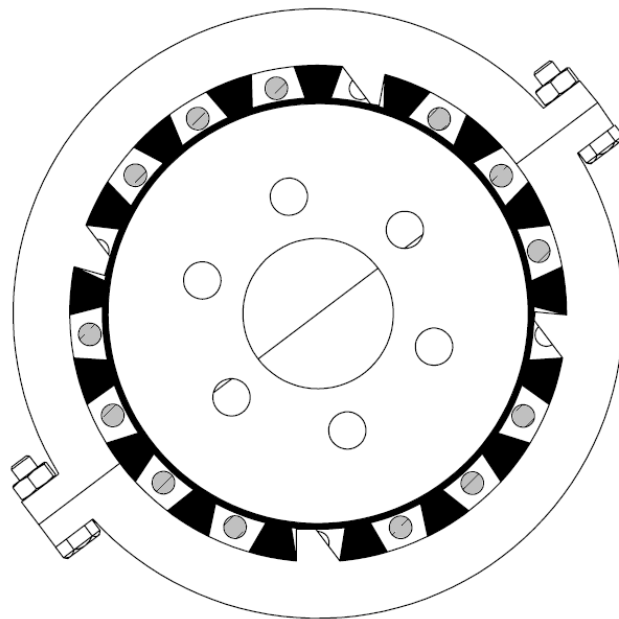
Vue du dessus du montage des pièces polaires
